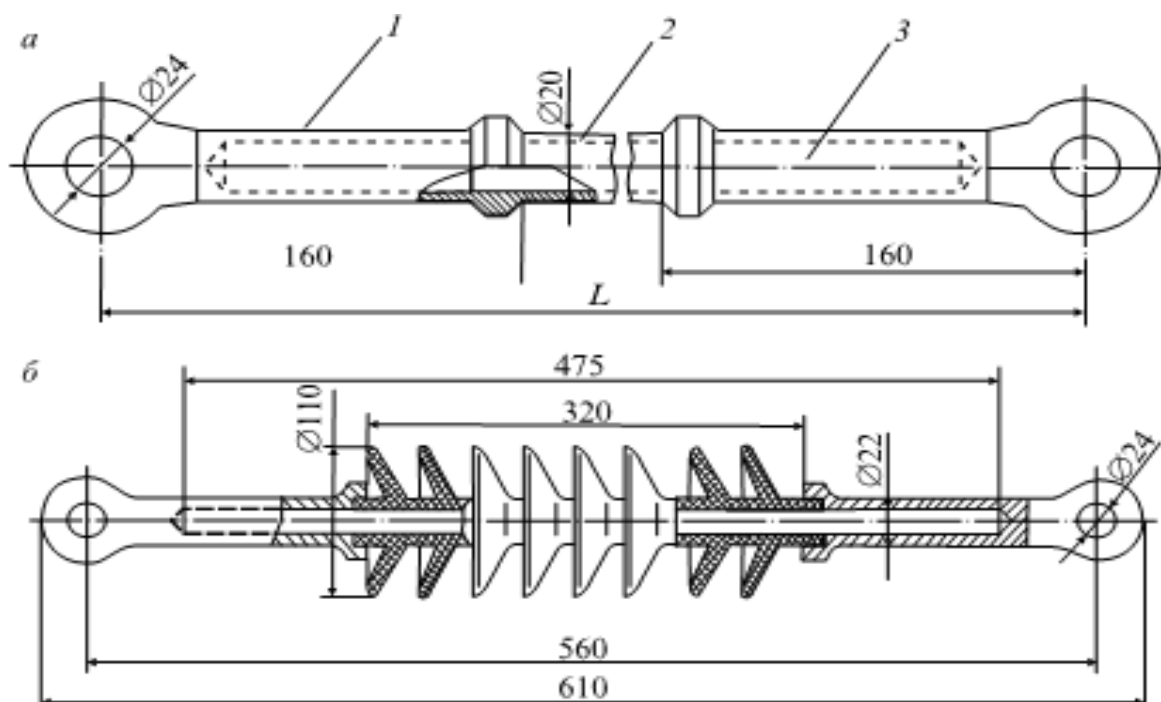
Полимерные натяжные изоляторы: а – НСФт 120/1,2 с фторопластовой защитной трубкой; б – НСКр 120/0,95 с ребристым защитным чехлом из кремнийорганической резины; 1 - оконцеватель; 2 - защитная трубка; 3 – полимерный стержень.
